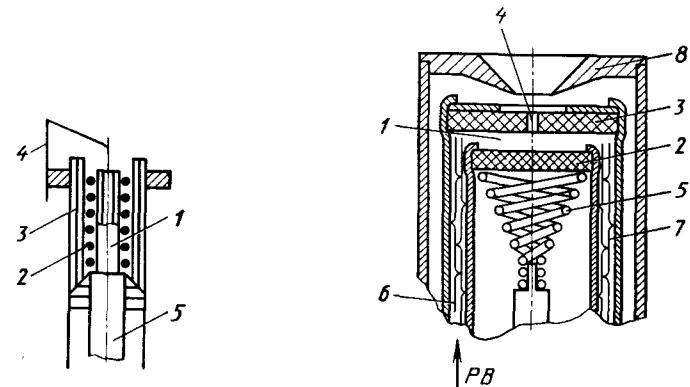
Газоразрядный плазменный нейтрализатор:
